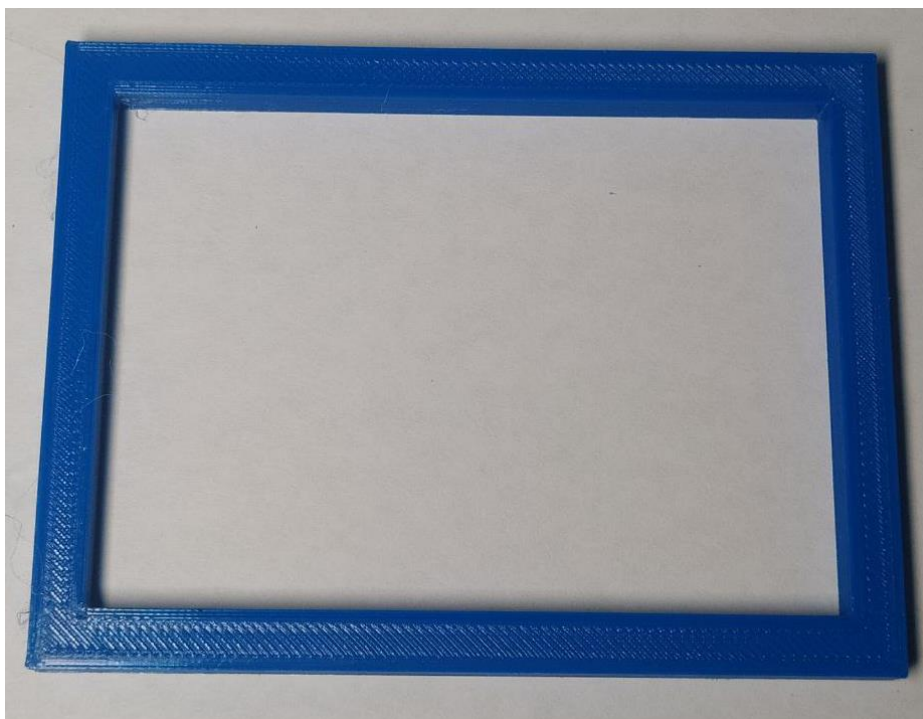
Нижня частина корпусу ванни для фотополімеру
